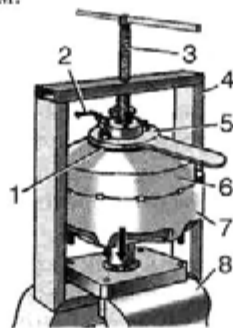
Приспособление 6999-7567 для разборки и сборки вакуумного усилителя:
